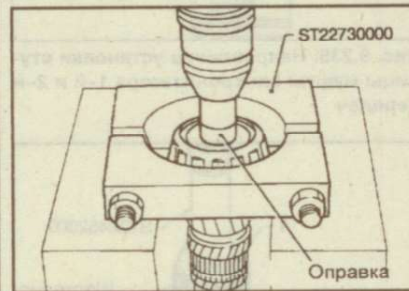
Снятие переднего подшипника с вторичного вала
